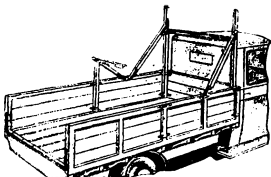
Детали крепления съемных боковин в кузове, приспособленном для перевозки овощей и фруктов.
